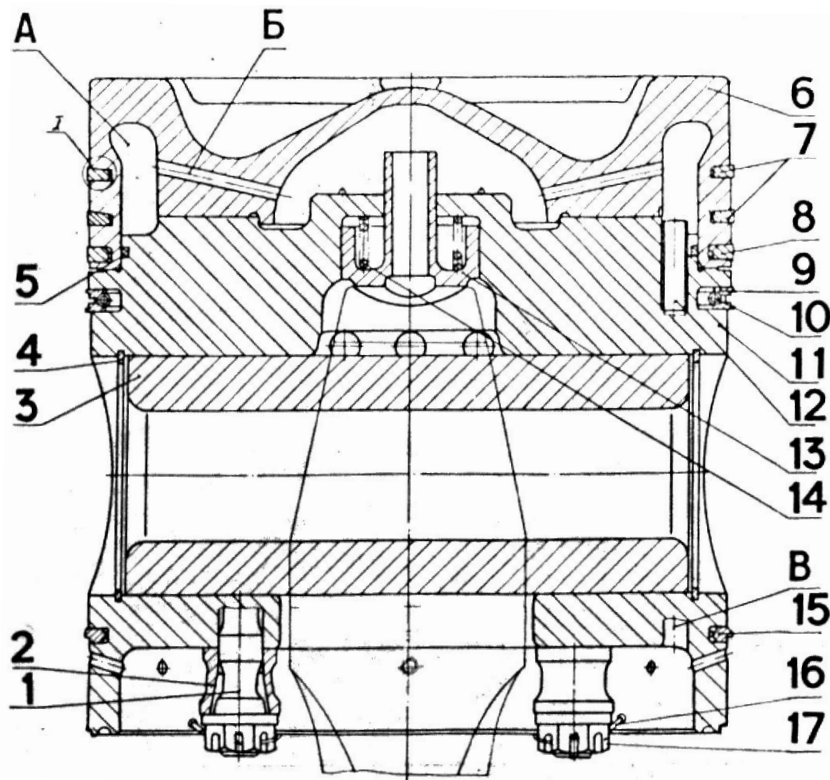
Поршень: 1 – шпилька; 2 – втулка; 3 – палец поршневой; 4 – кольцо стопорное; 5 – кольцо уплотнительное; 6 – головка поршня; 7, 8 – кольца компрессионные; 9, 15 – кольца маслосъемные; 10 – экспандер; 11 – тронк; 12 – трубка; 13 – стакан; 14 – пружина; 16 – проволока; 17 – гайка; А – полость охлаждения; Б – отверстие подвода масла в полость охлаждения; В – канал для слива масла из полости охлаждения
